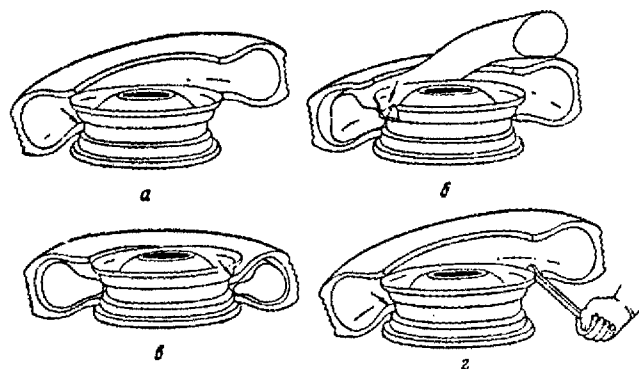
Порядок монтажа и демонтажа шины: а – заправка первого борта покрышки; б – заправка камеры в обод колеса; в – заправка второго борта покрышки; г – демонтаж покрышки
